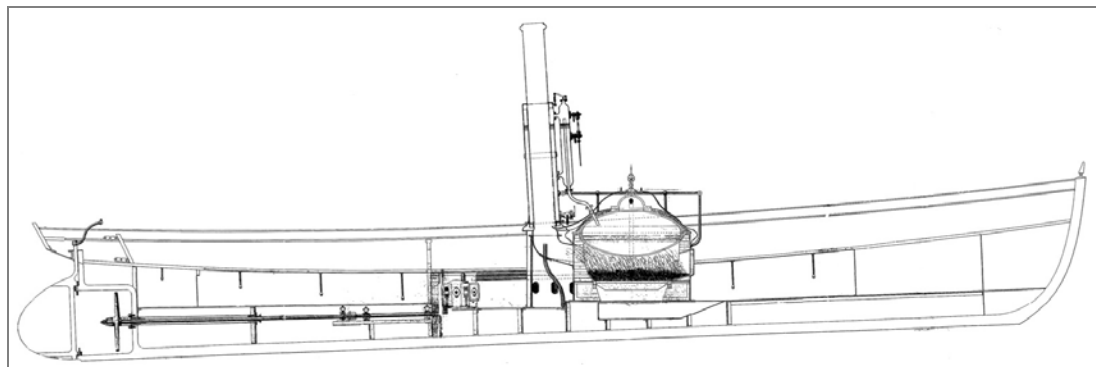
CANOT A VAPEUR, VUE DE TRIBORD COUPE DU PLAN DE 1860
